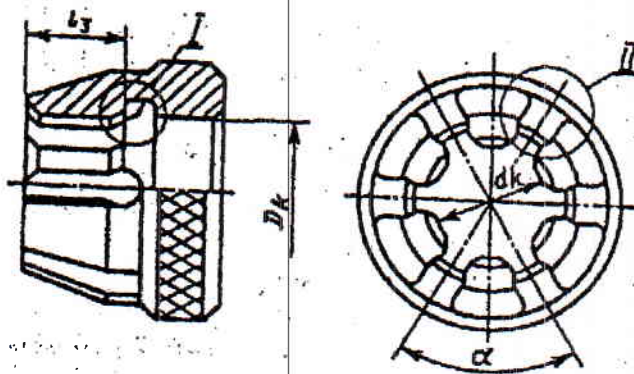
Комплексный калибр-кольцо для контроля размеров шлицевого прямобочного вала
